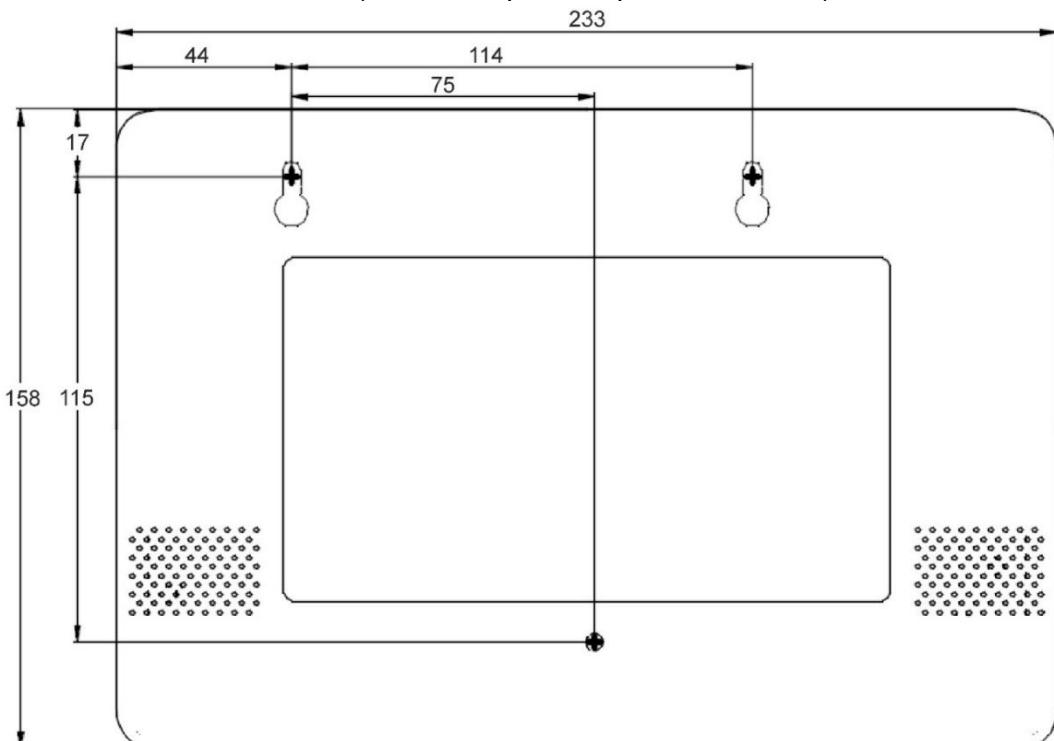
Разметка отверстий для крепления прибора КОП-01 исп.2, КОП-05 (вид со стороны передней панели)
